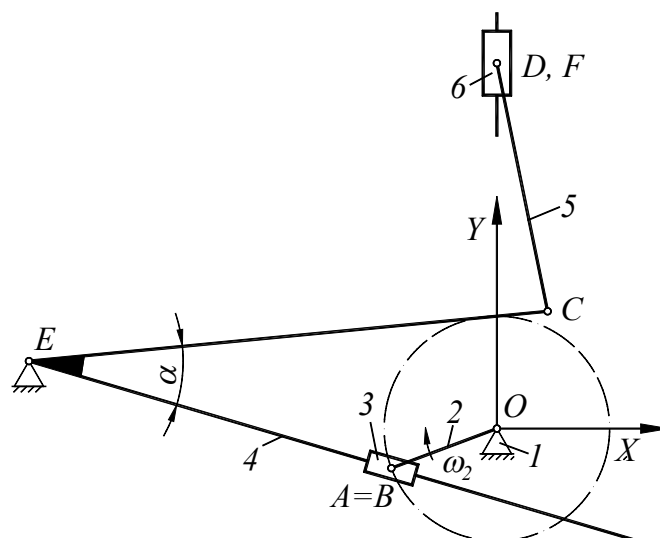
Кинематическая схема механизма долбежного станка с качающейся кулисой
